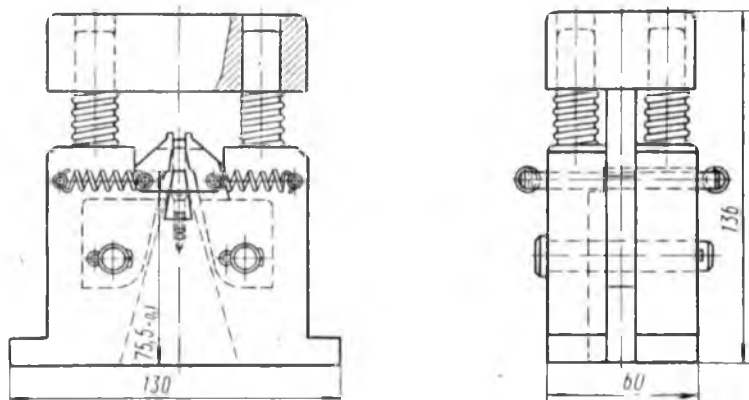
Головка для гибки насечкой (к станку рис. 1.13)
